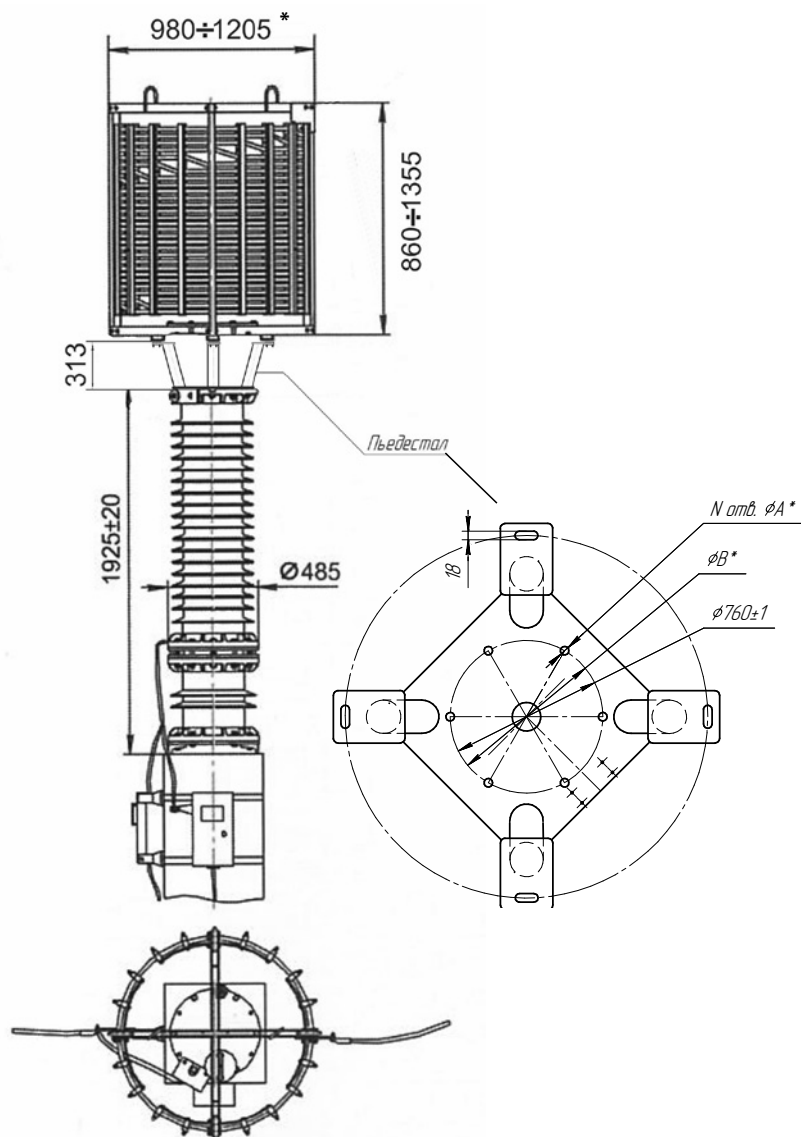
Установка заградителей ВЗ-630, ВЗ-1250, ВЗ-2000 на конденсатор связи усиленного исполнения СМА - 110/√3 - 6,4 УХЛ1.
